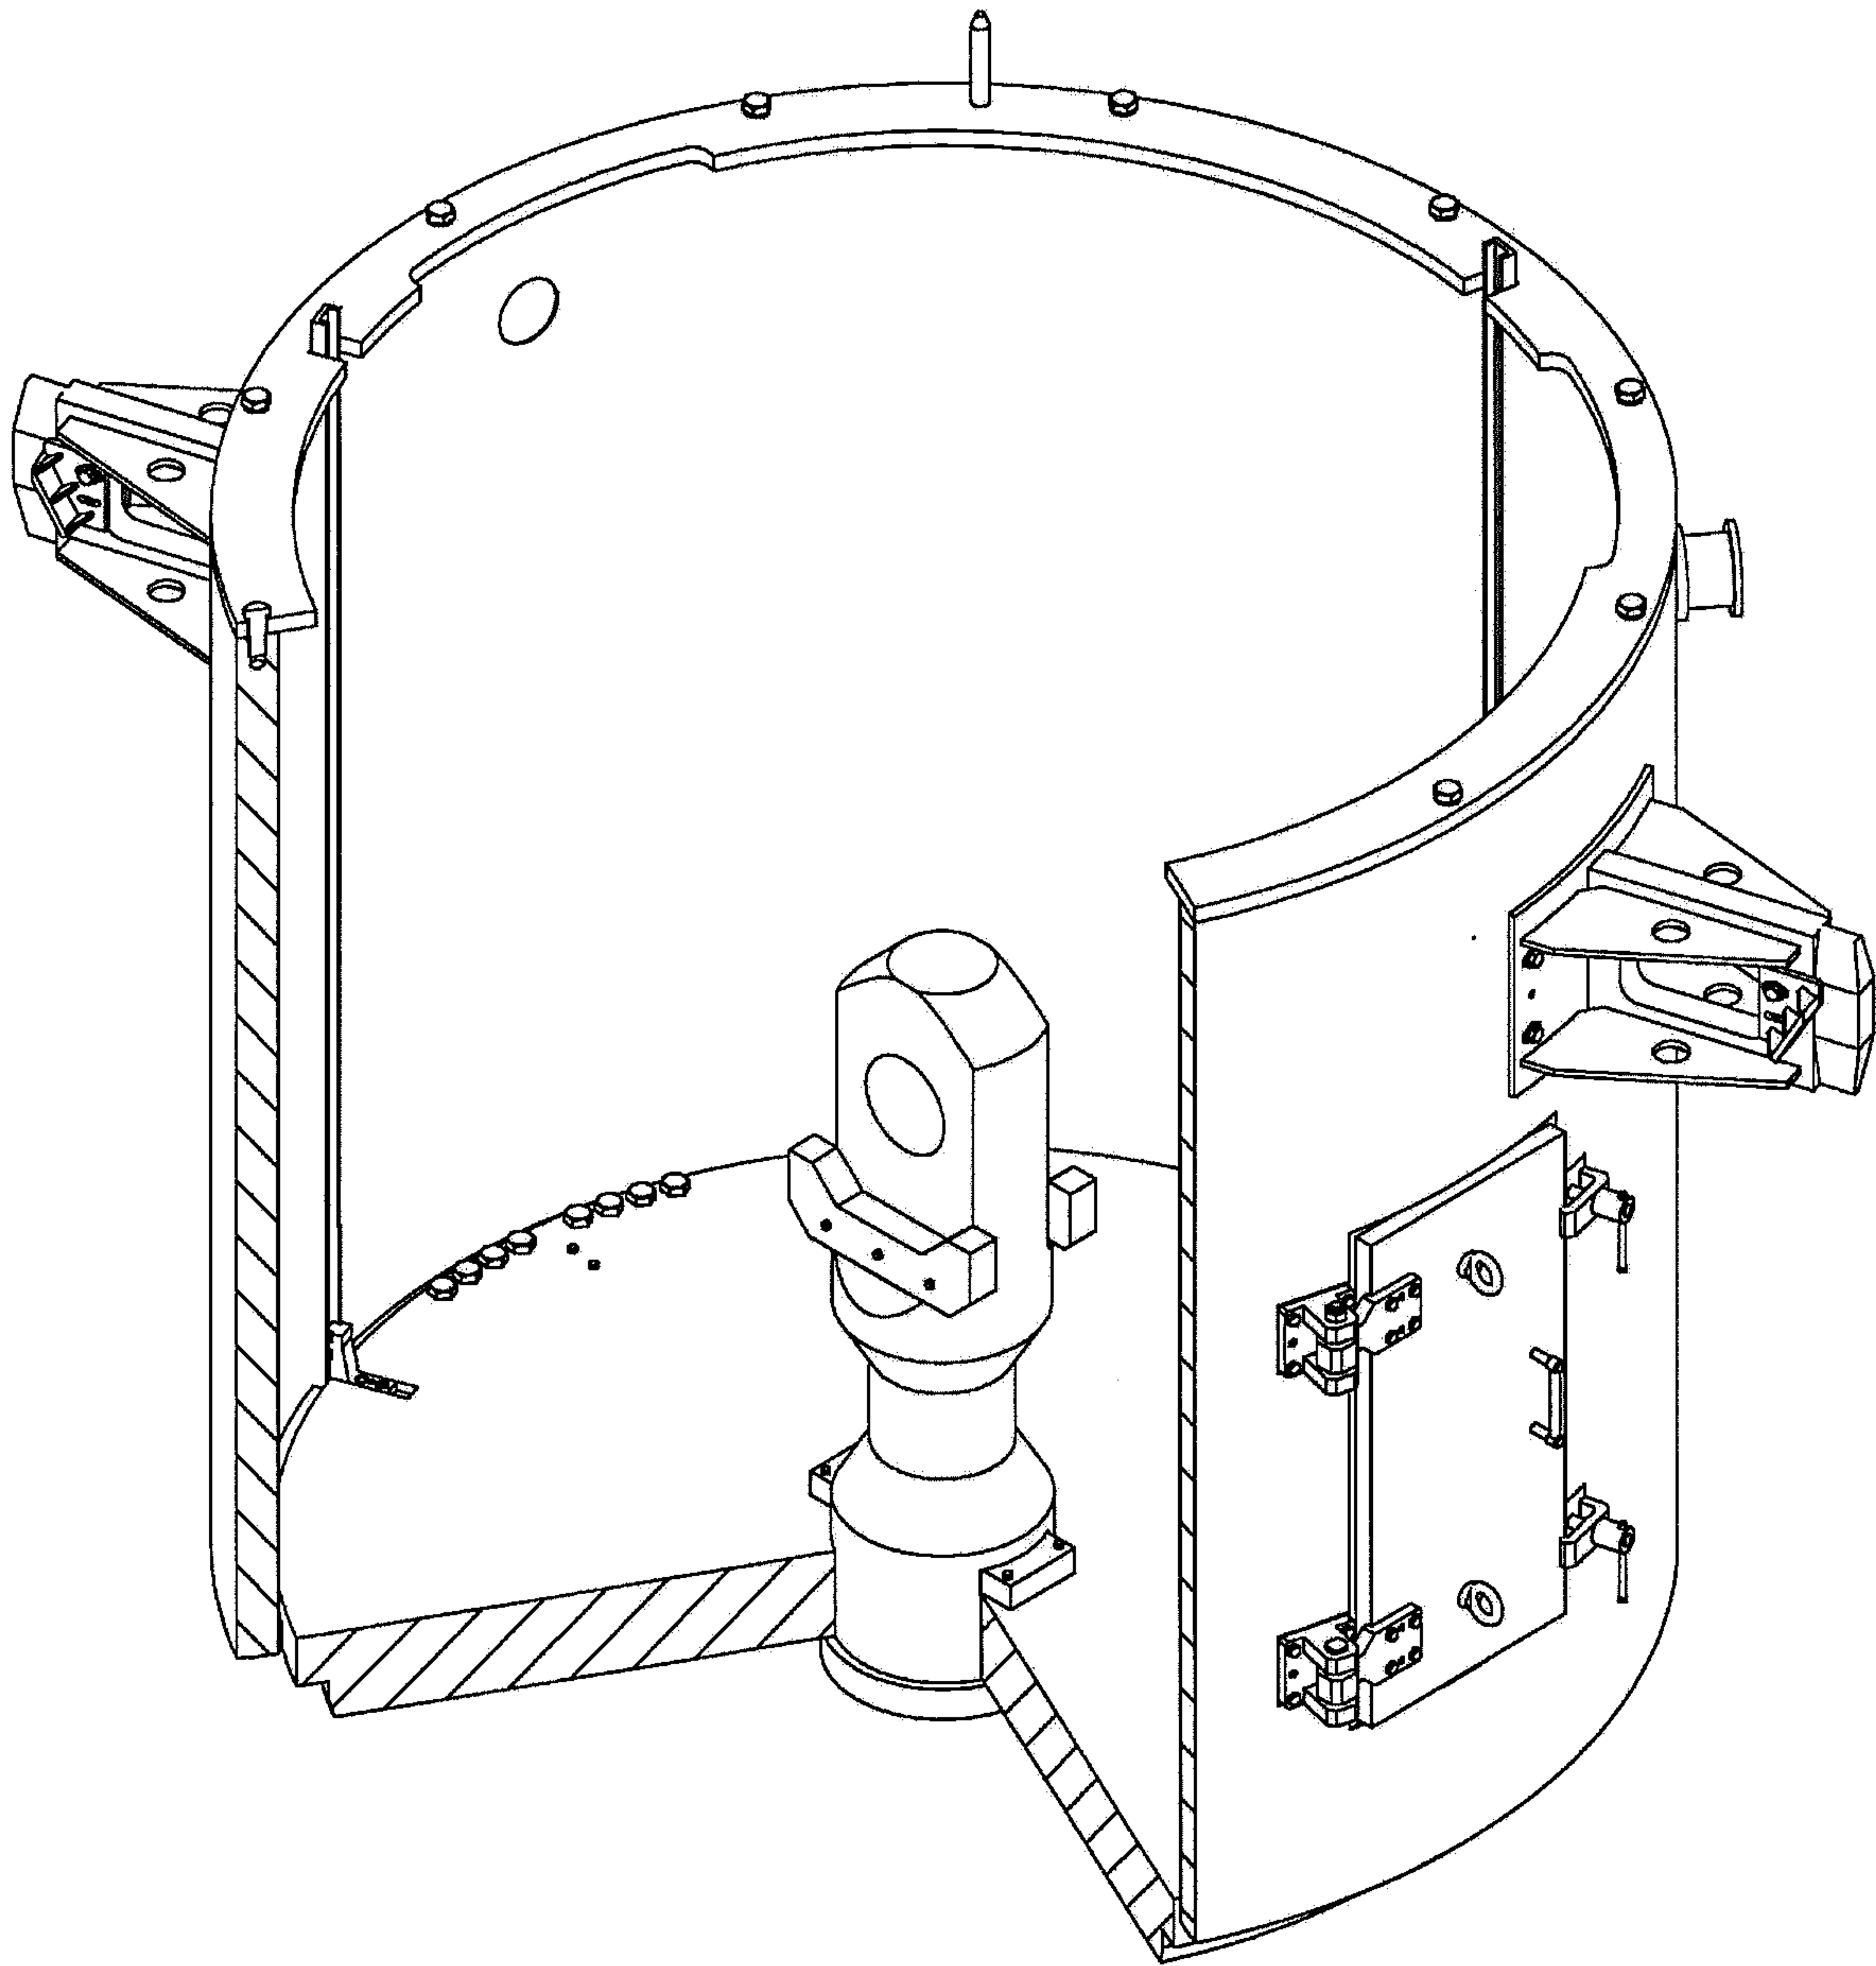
Устройство для транспортировки шахты внутрикорпусной
